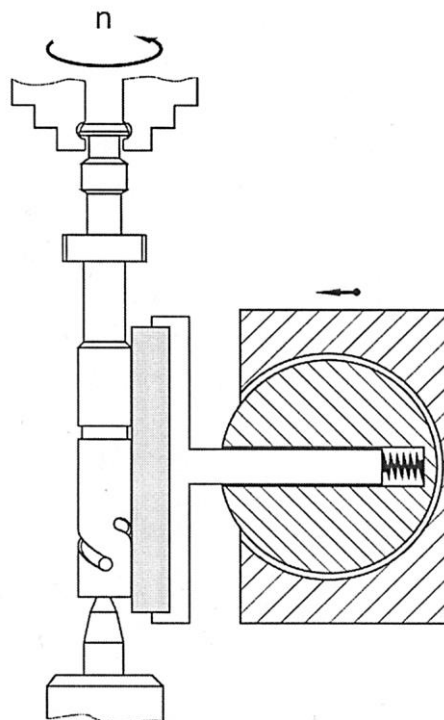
Схема устрою для обробки поверхні штока шліфуванням.
